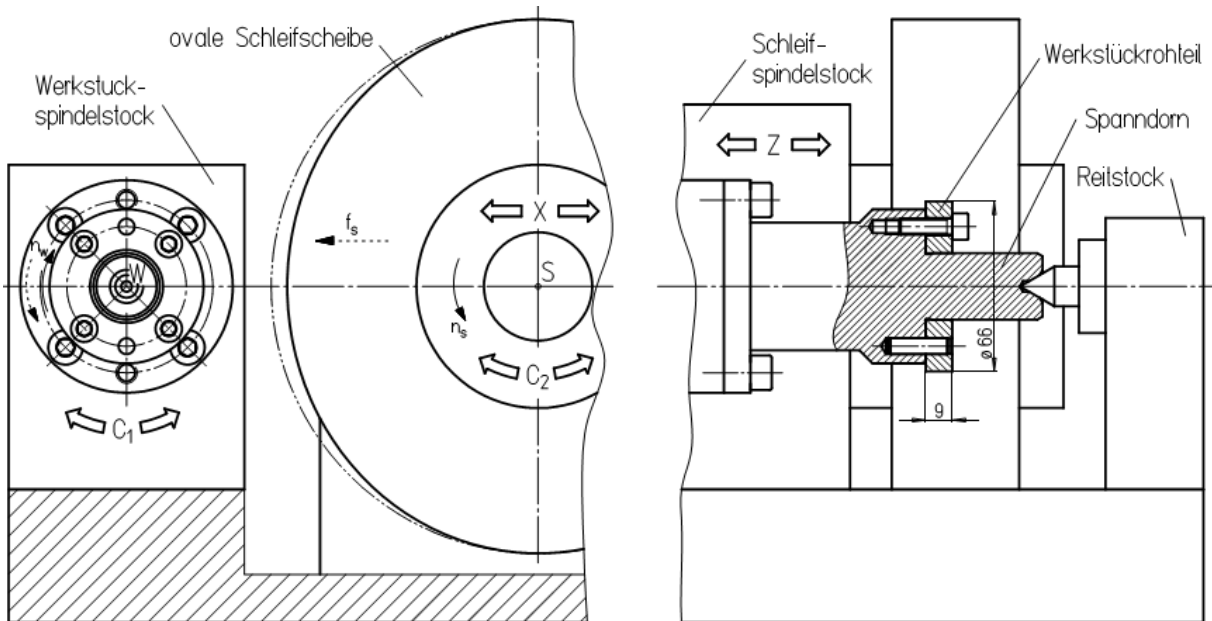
Versuchsaufbau bei der Verwendung vorgeformter, formgebundener Werkzeuge
